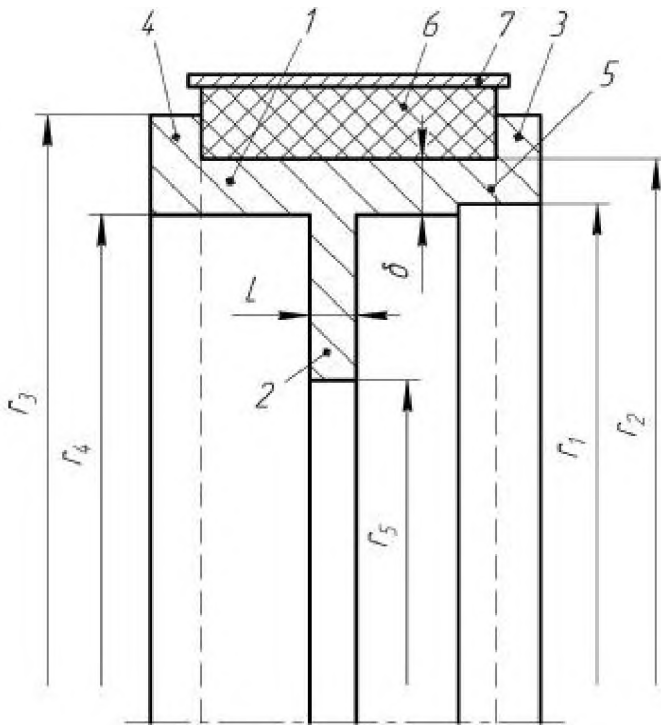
Конструктивные параметры тормозного шкива и его элементы: 1 – цилиндрическая оболочка; 2 – фланец; 3, 4 – реборды; 5 – цилиндрический диск; 6 – фрикционная накладка; 7 – тормозная лента
